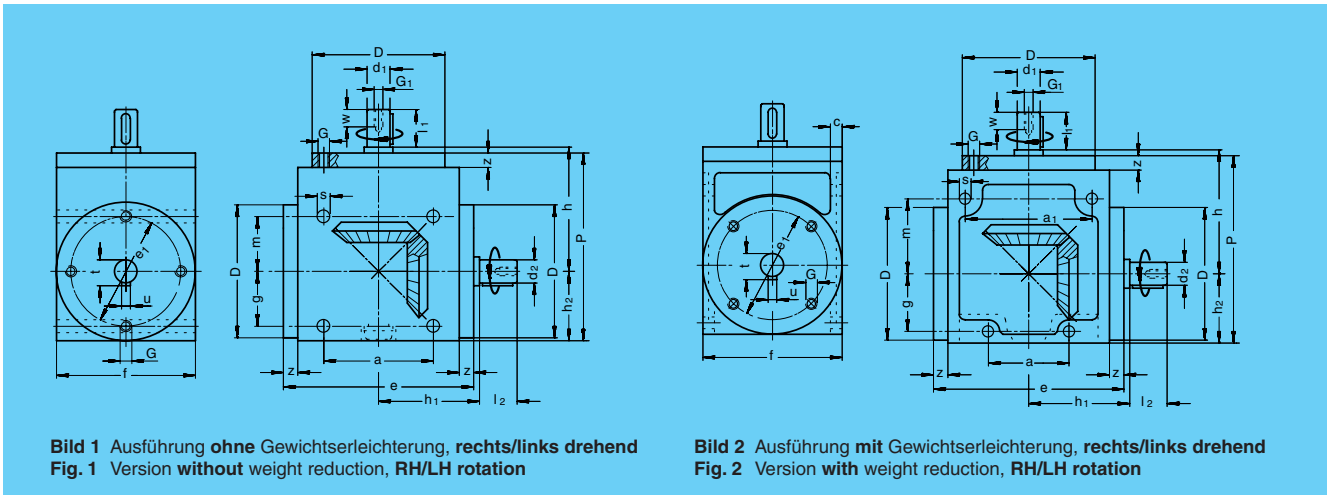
Ausführung ohne Gewichtserleichterung, rechts/links drehend
